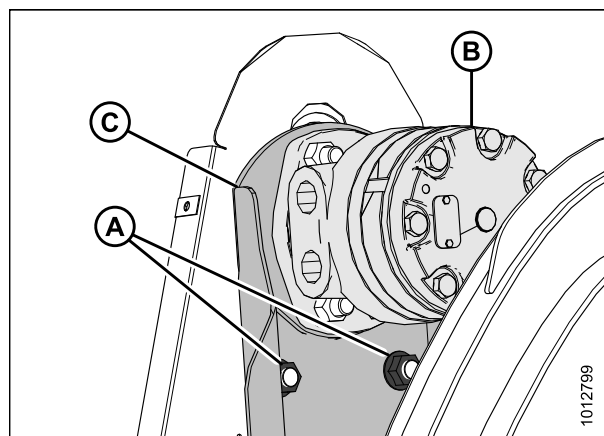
Изображен привод одинарного мотовила — привод сдвоенного мотовила имеет такую же конструкцию
